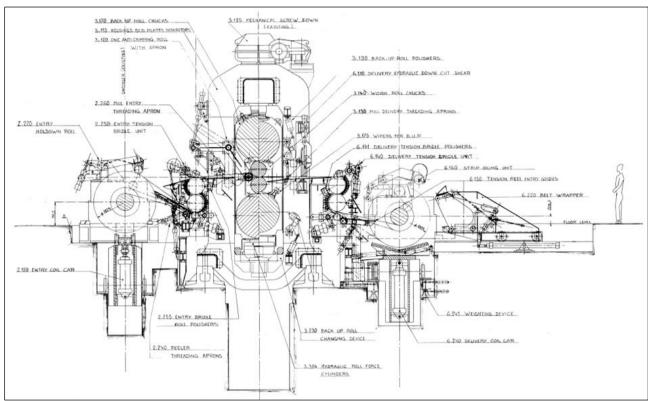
Vista frontal del Laminador (PL 29-6155)
